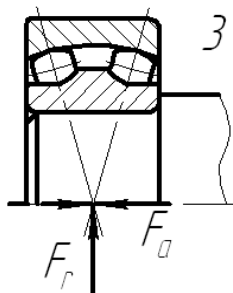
Радиальный самоустанавливающийся роликоподшипник
